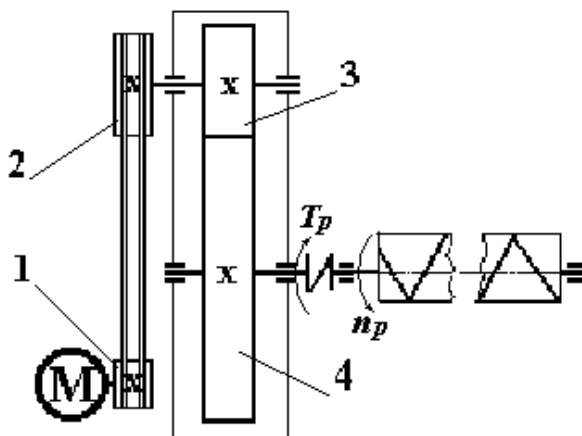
Кинематическая схема привода шнекового транспортера
